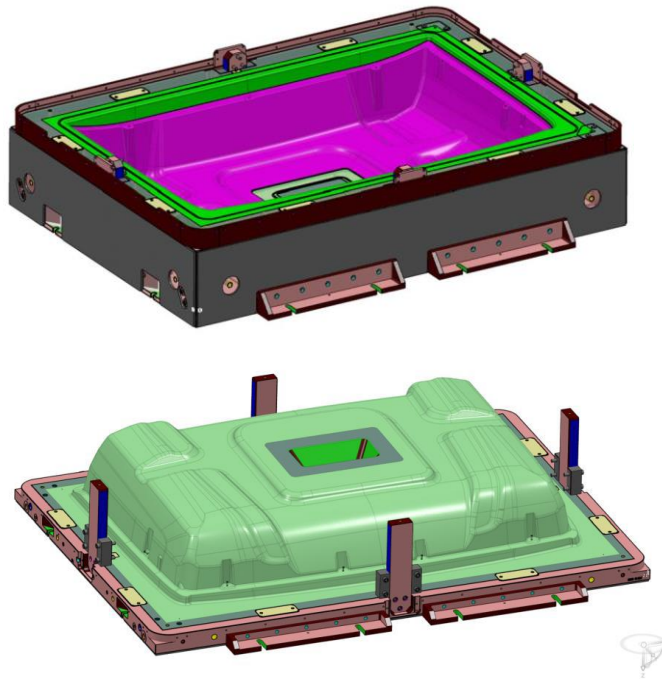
CAD-Stand des LFI-Werkzeuges
